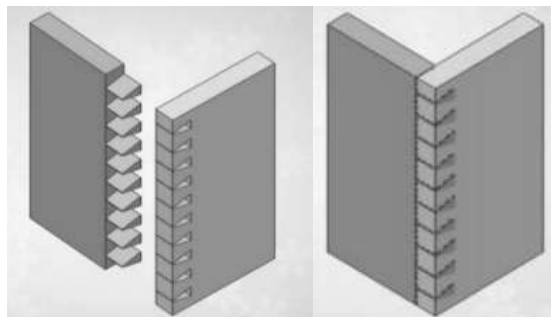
º Técnica “Junta de Montagem Fissurada” (Fonte: Comelli, 2018, p.127)
